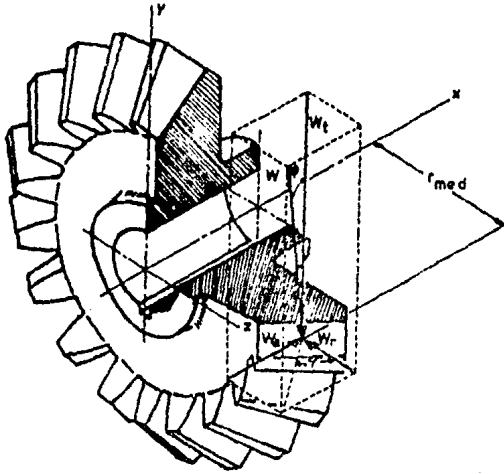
FUERZAS ENTRE DIENTES DE ENGRANES CONICOS.
